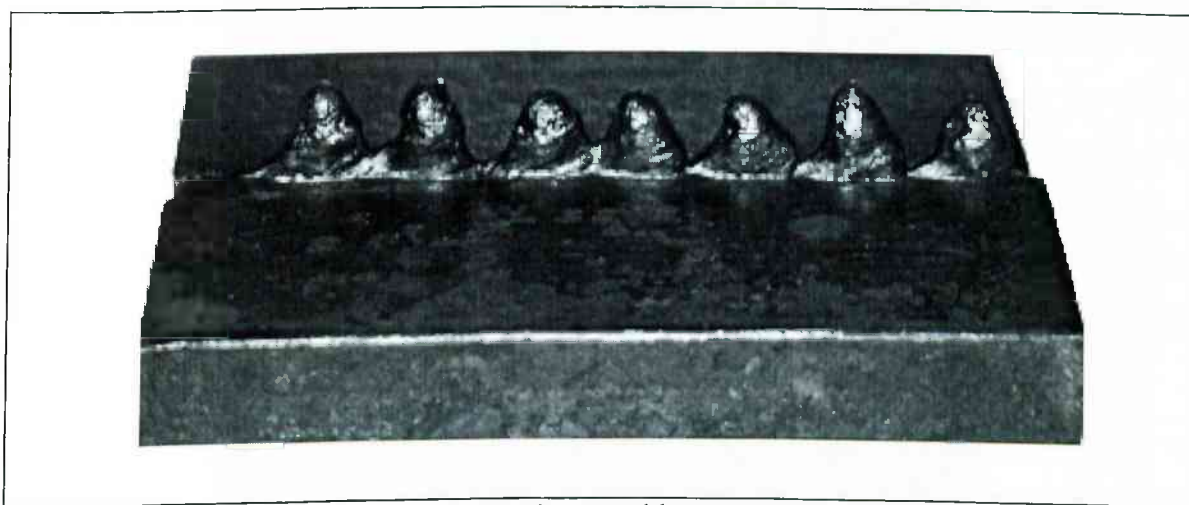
Defeito “humping” observado em soldas com penetração excessiva.
